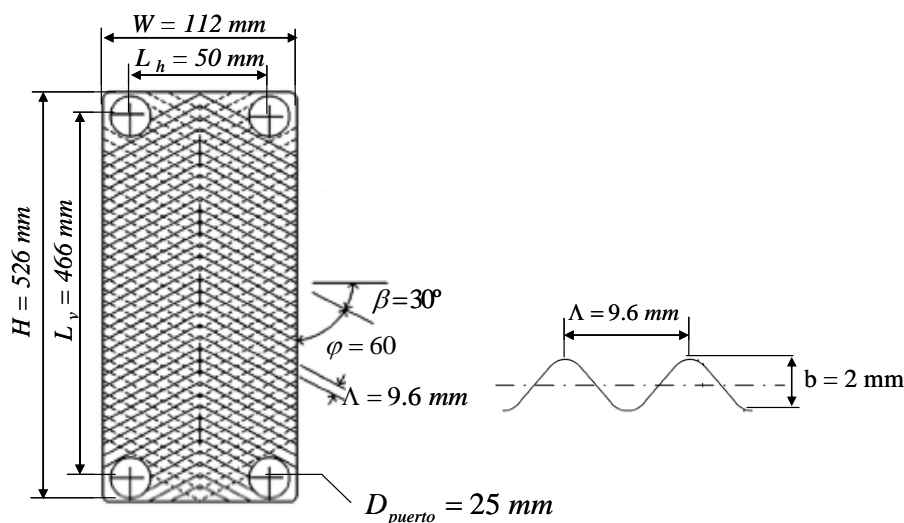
Dimensiones geométricas del intercambiador de placas ensayado en esta tesis.
